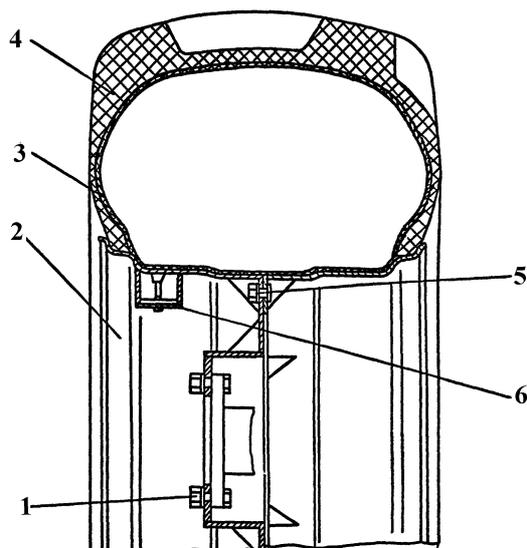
Установка колеса: 1, 5 – гайки; 2 – обод; 3 – камера; 4 – покрышка; 6 – крышка
